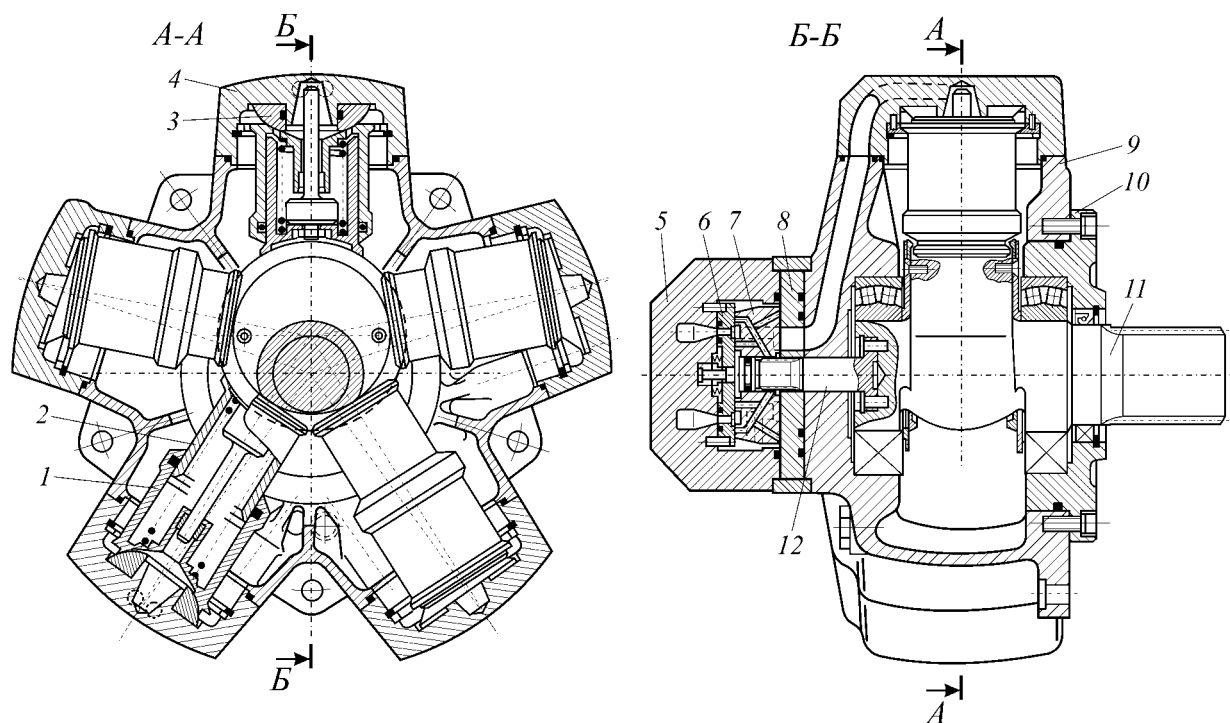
Радиально-поршневой гидромотор серии МР: 1 – гильзы цилиндров; 2 – поршни; 3 – сферические опоры; 4 – крышки; 5 – торцевая крышка; 6 – втулка; 7 – распределительный диск; 8 – втулка; 9 – корпус; 10 – крышка; 11 – вал; 12 – промежуточный вал
